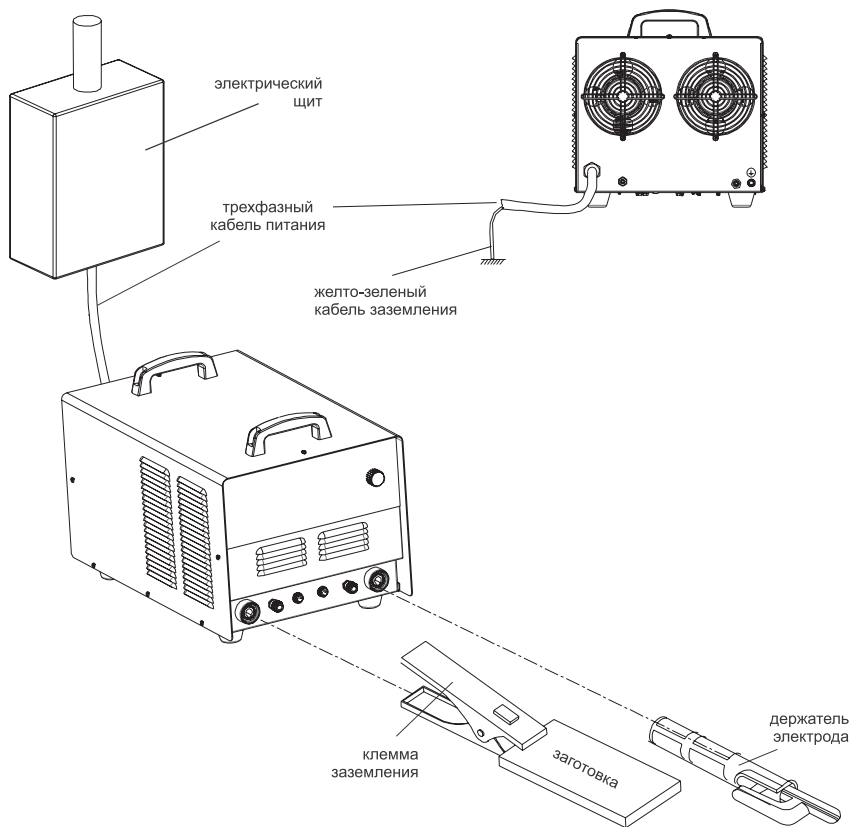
Типовая схема установки оборудования при ручной дуговой сварке (ММА)
